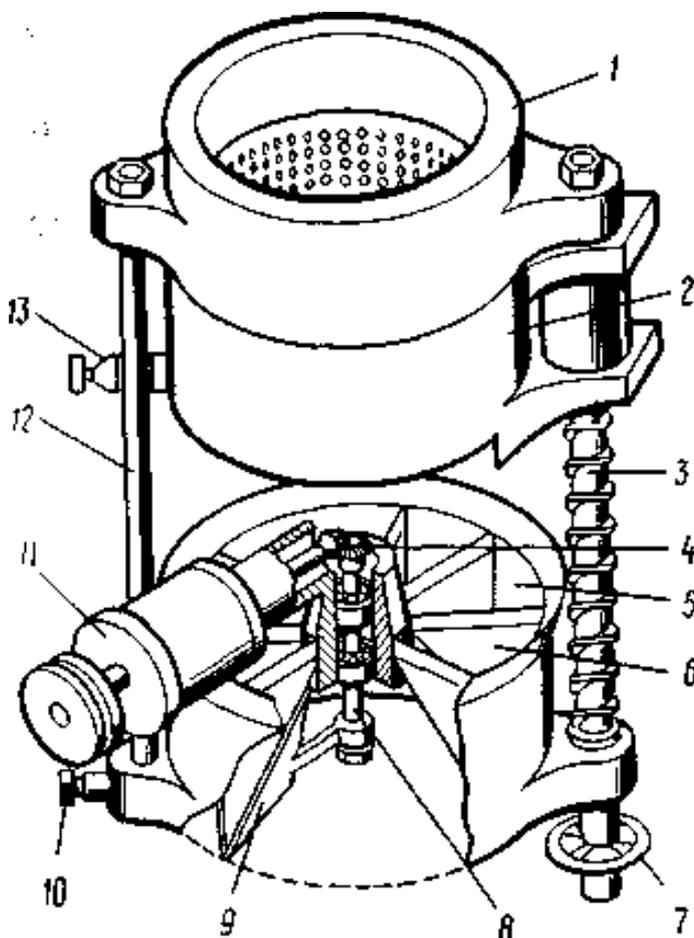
Механизм для резки «перьев» к прессу типа ЛПШ:
